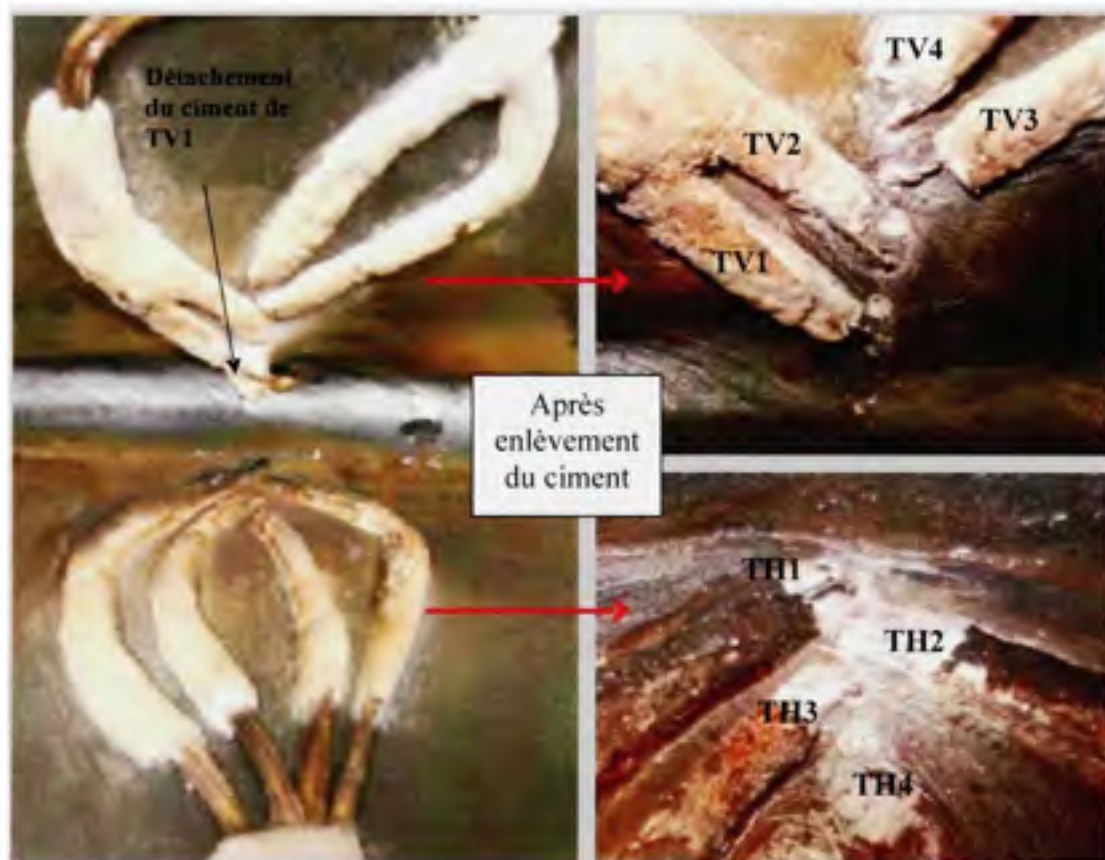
Thermocouples après soudage (échelle sur la figure 2.7)
